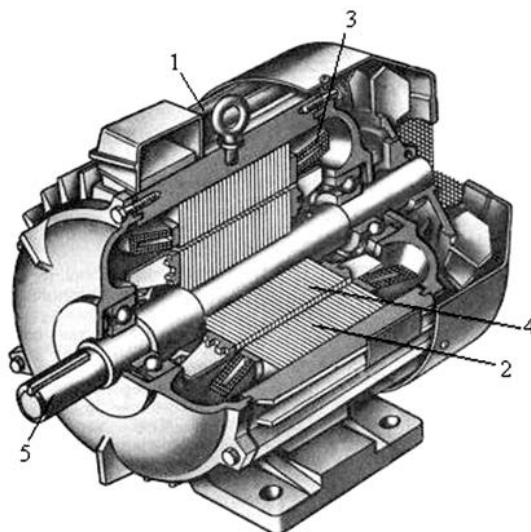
Асинхронний двигун «наскрізної» конструкції: 1 – корпус ЕД, 2 – пластини осердя статора, 3 – обмотка статора, 4 – пластини осердя ротора, 5 – вал
